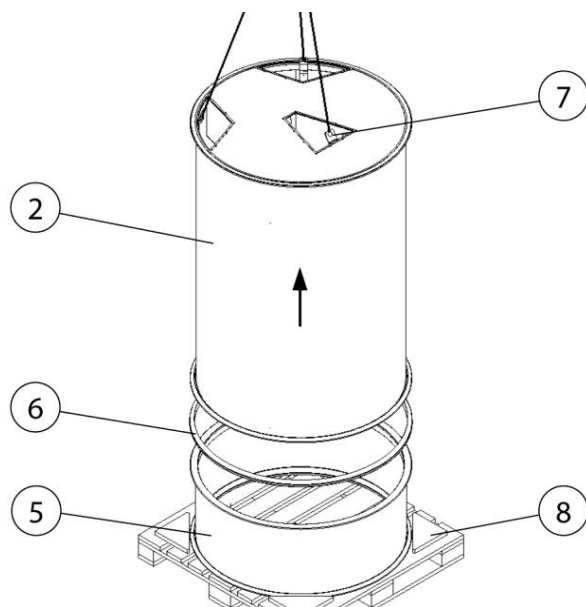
Levantar la parte del filtro del adaptador de transporte
